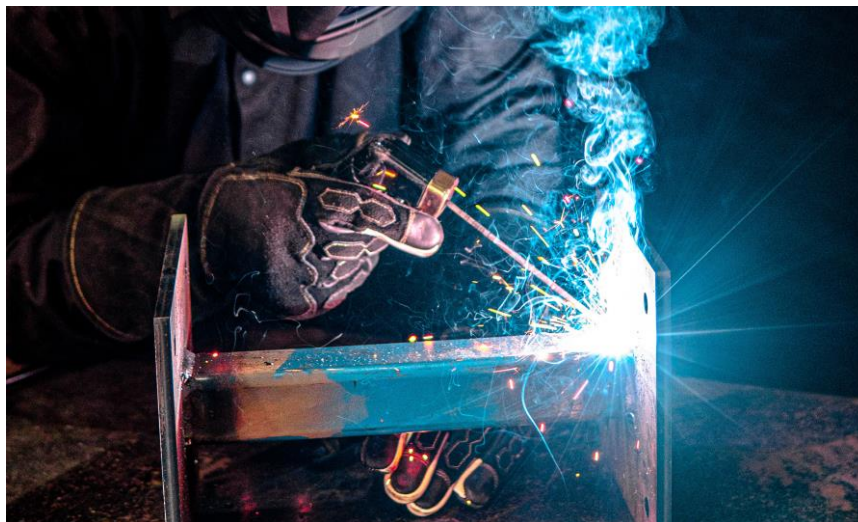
Ilustração do processo de soldadura por eléctrodo revestido [33]
